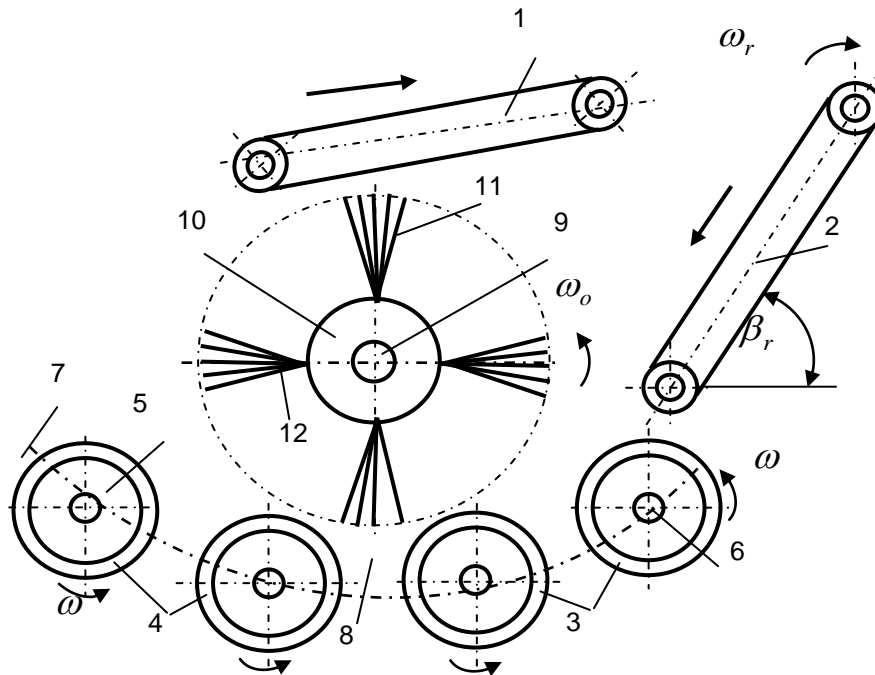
Конструктивна схема комбінованого очисника: 1 – транспортер; 2 – гірка; 3, 4 – права та ліва система; 5 – шнек; 6 – вісь обертання; 7 – нижня вітка еліпса; 8 – жолоб робочого русла; 9 – вал; 10 – барабан; 11 – пружні очисні елементи; 12 – пучки ворсу
